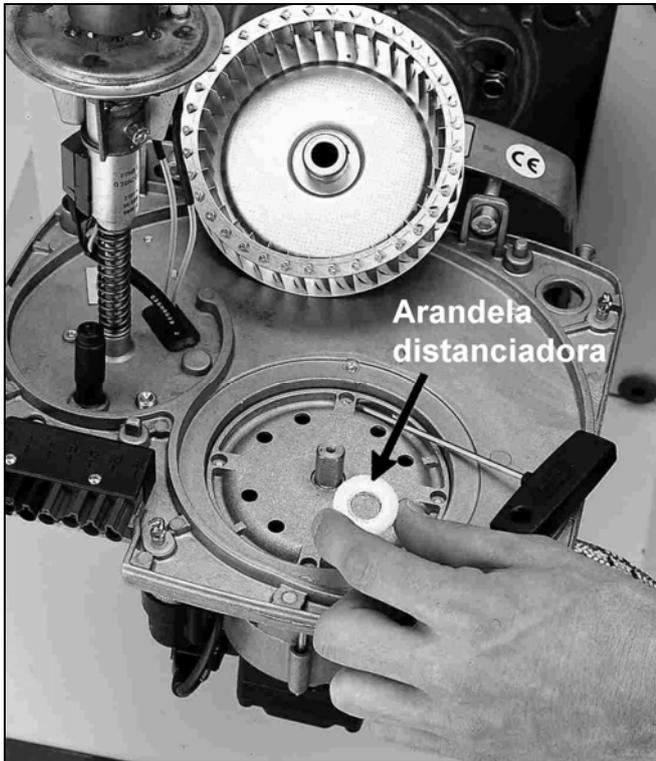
Utilizar la arandela distanciadora para el posicionamiento axial del rodetes del soplador
